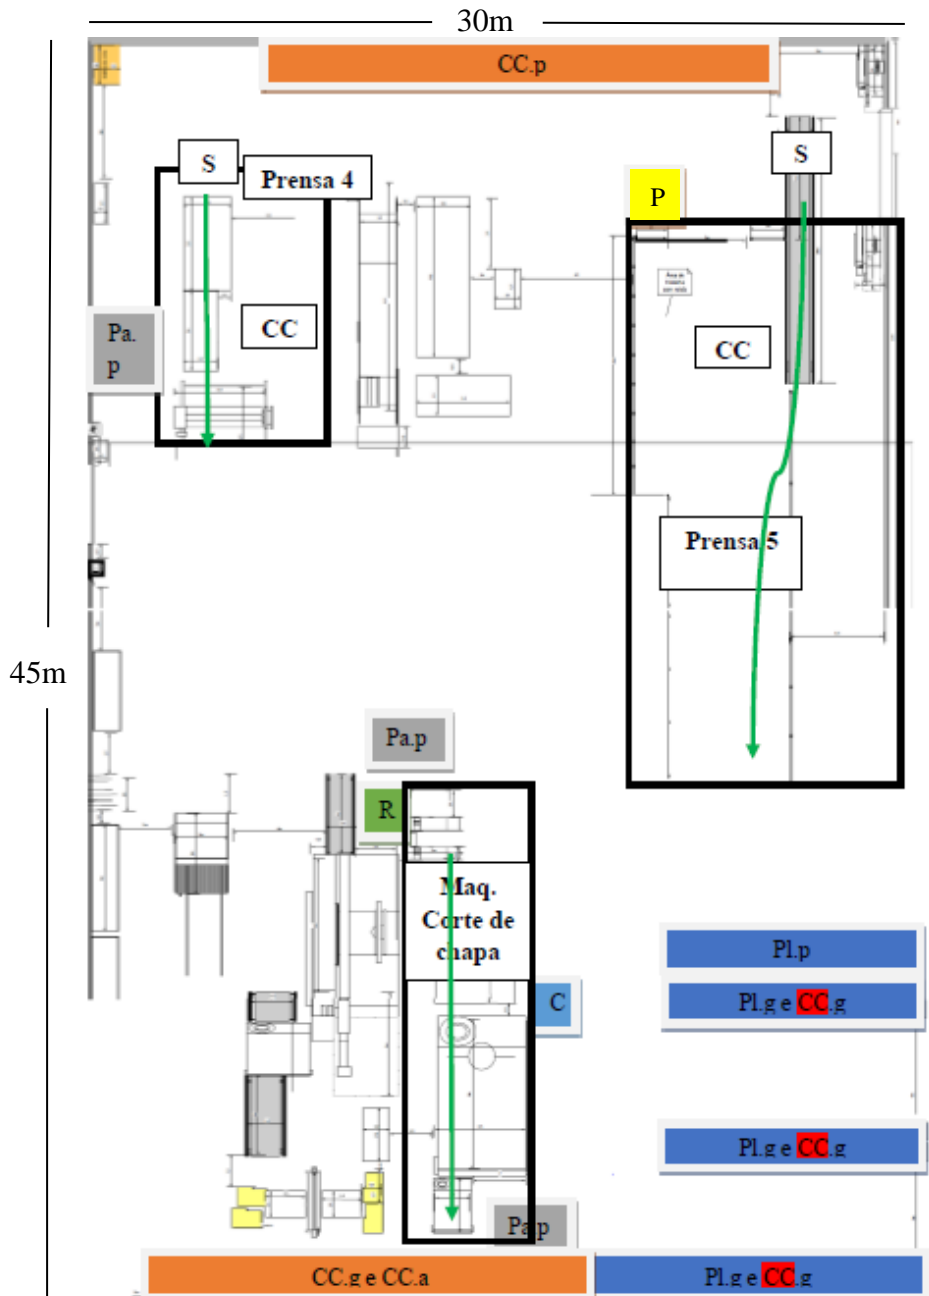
Layout do pavilhão de corte e colagem de chapa
